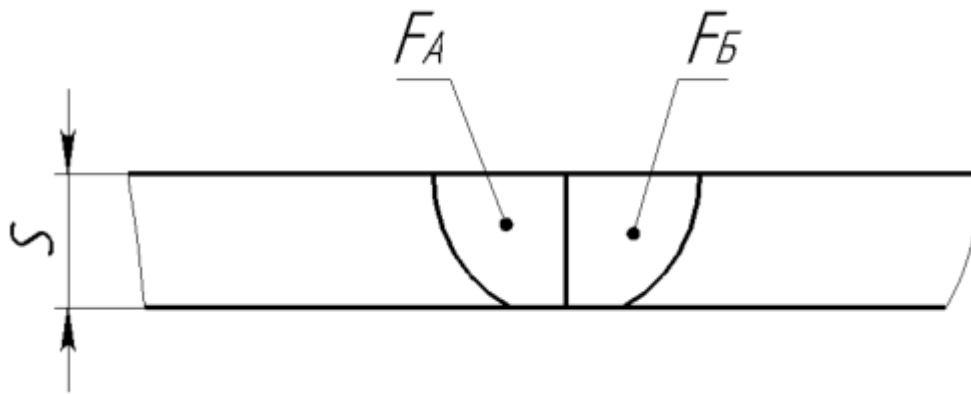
Сварка листов 1–1 мм
